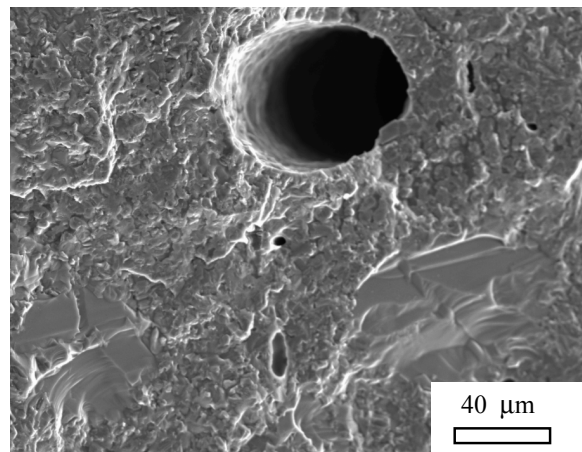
Superficie de fractura del EU ensayado a flexión a 25 °C.
